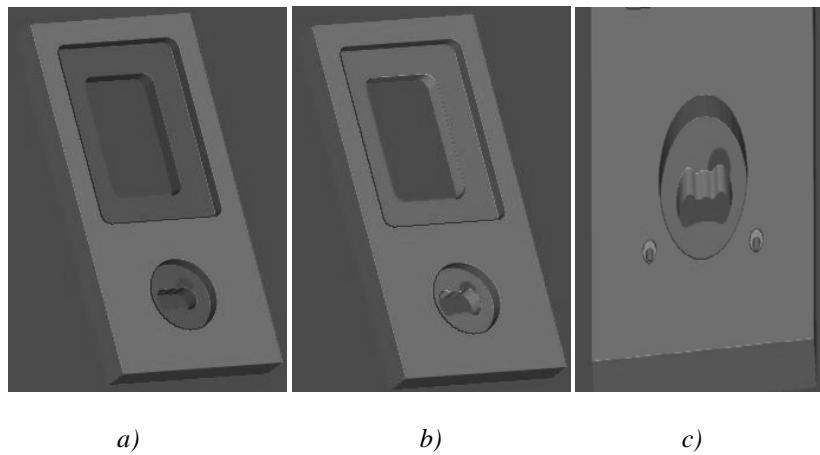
a) Placa porta punzones maquinada con cortador de 12.7 [mm]. b) Placa porta punzones maquinada con cortador de 4.76 [mm]. c) Placa porta punzones maquinada con cortador de 3.175[mm].
